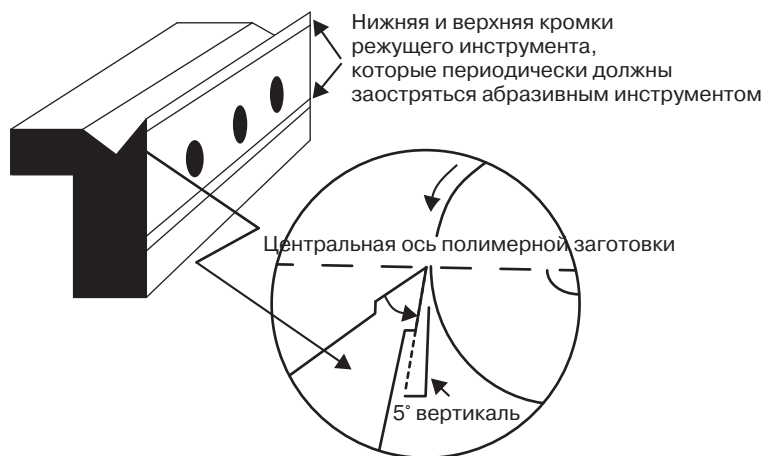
Режущий инструмент для строгания пленки (ленты) из цилиндрической заготовки
